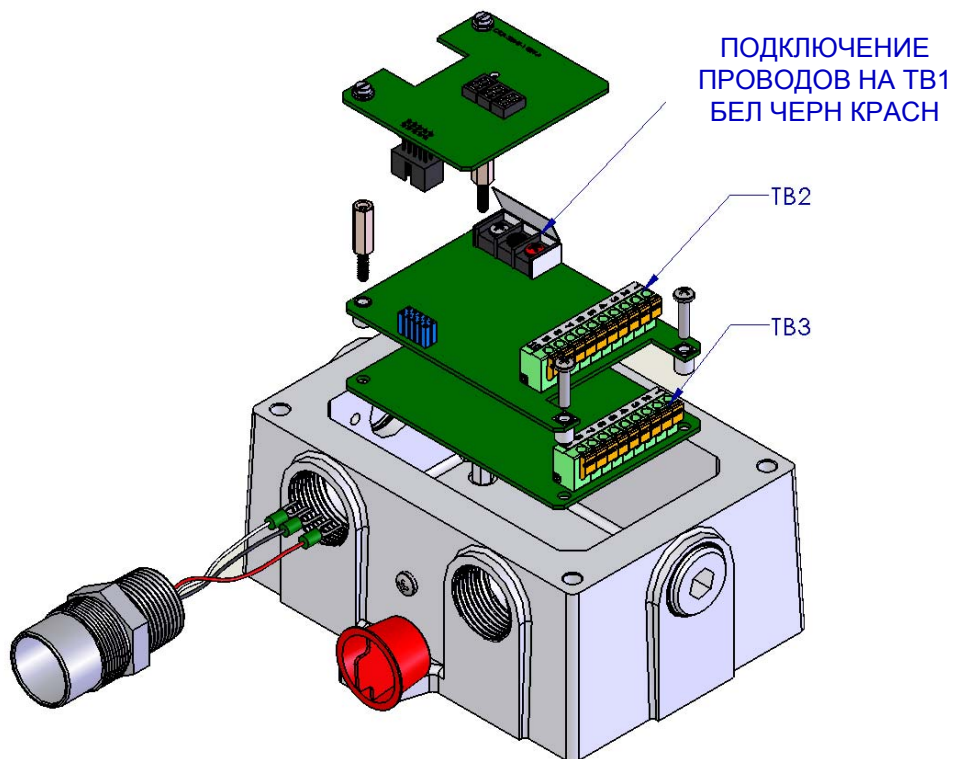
Расположение клеммной колодки газоанализатора S400CH
